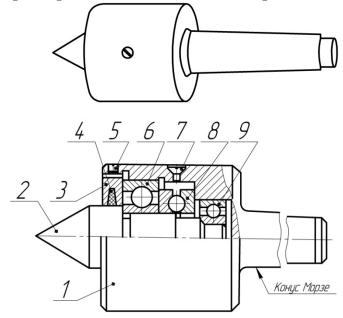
Задние вращающиеся центры нормальной серии с конусом Морзе: 1 – корпус; 2 – центр; 3 – гайка; 4 – сальник; 5 – стопорный винт; 6, 9 – радиальные шарикоподшипники; 7 – винт; 8 – упорный шарикоподшипник
